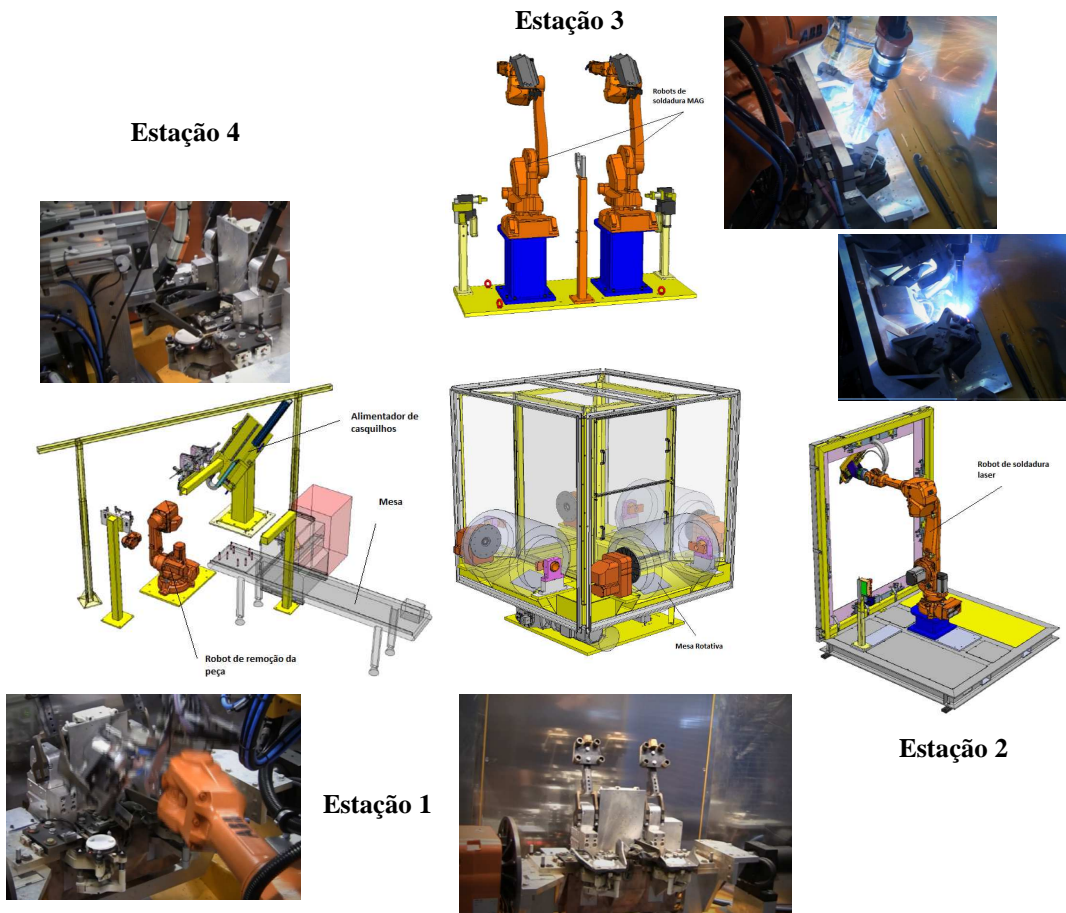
Fases do processo de soldadura híbrida [AWL 2012]
